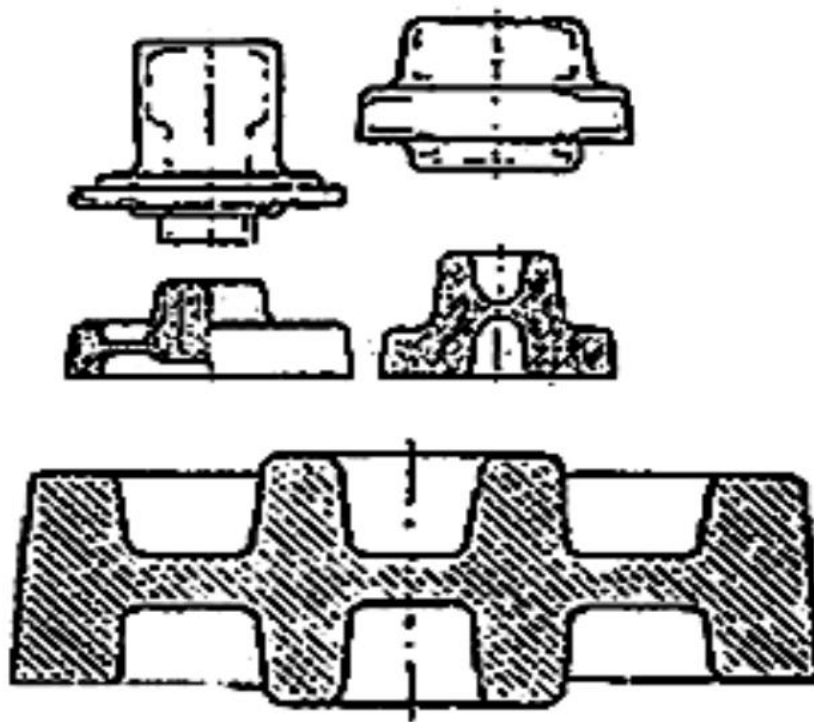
Типові штамповки, що виготовлені в закритих штампах
